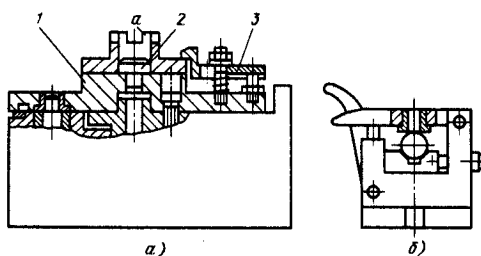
Наладочные приспособления: а — УНП; б — СНП
